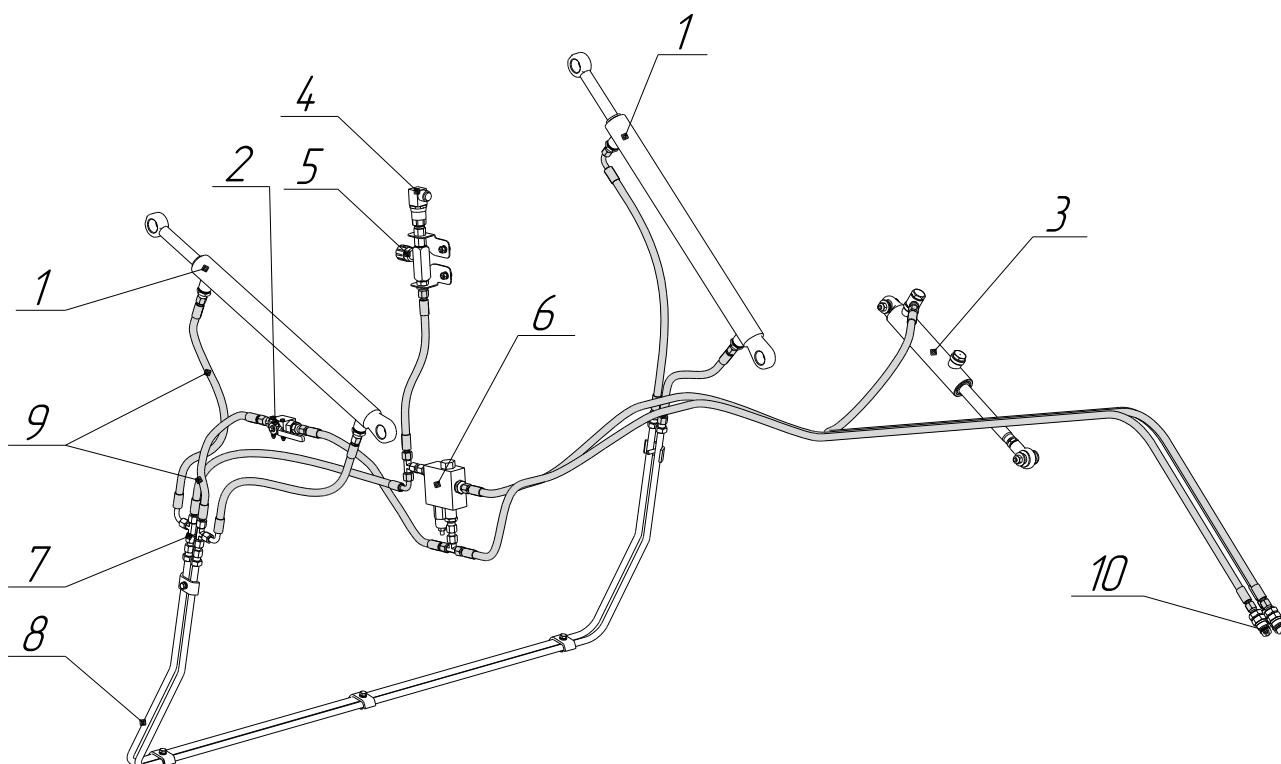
Гидравлическая система: 1 - гидроцилиндр открывания заднего корпуса; 2 – предохранительный кран с ручным управлением; 3 - гидроцилиндр подъема подборщика; 4 - преобразователь давления; 5 - дроссель с обратным клапаном; 6 - блок клапанов; 7 - муфта соединительная; 8 – трубопровод; 9 – РВД; 10 – разрывная муфта.
